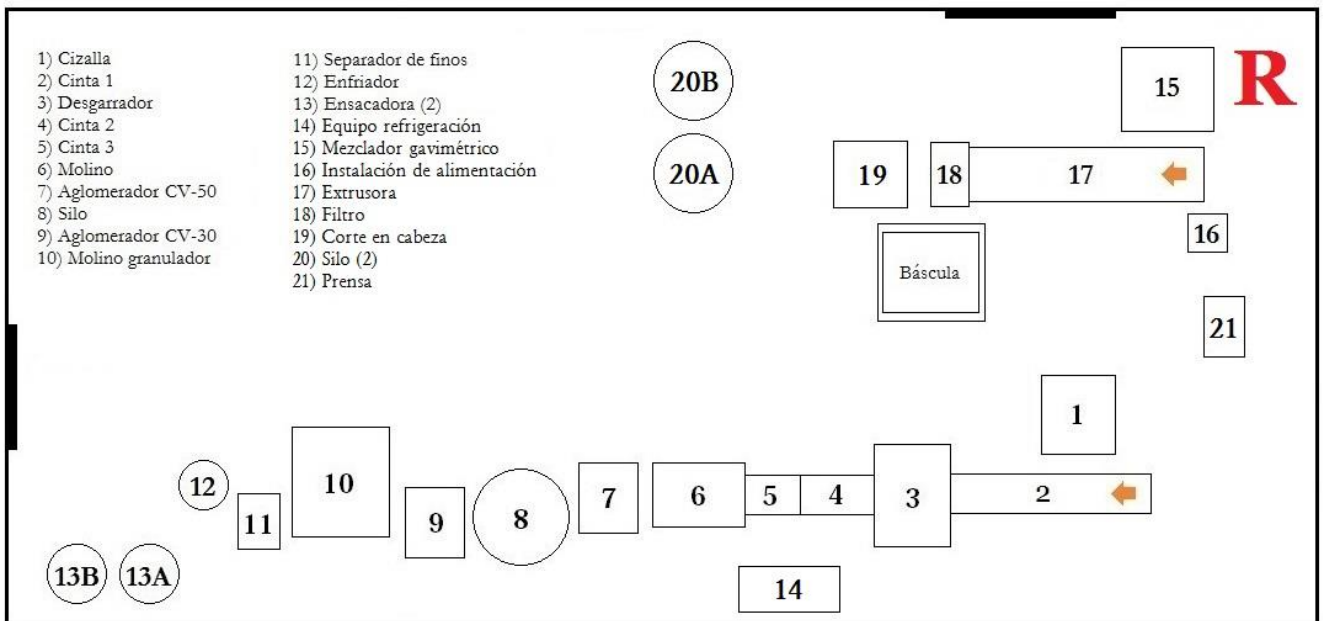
Distribución en planta de la zona de reciclado (R).
